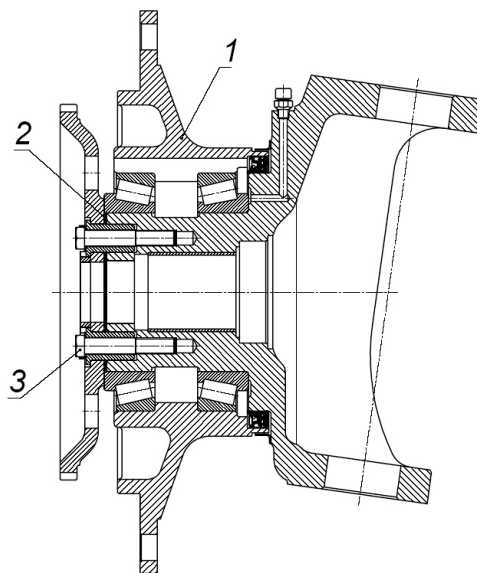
Ступица с кулаком колесного редуктора:
